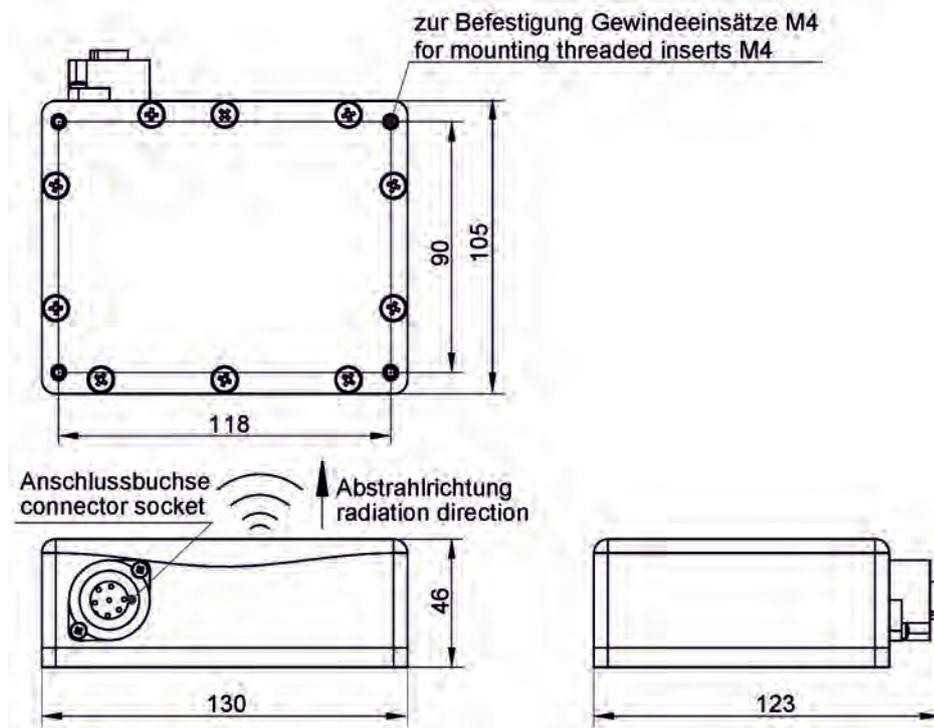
Abmessungen OFR-Radarsensor Typen H00/EVG im Sensorgehäuse
